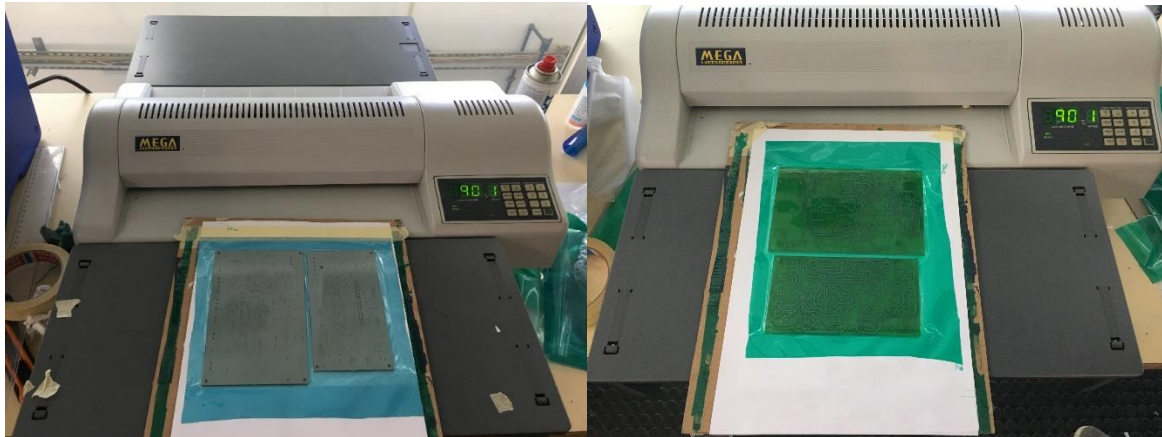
Laminadora com películas circuito (esquerda) e soldermask (direita)
